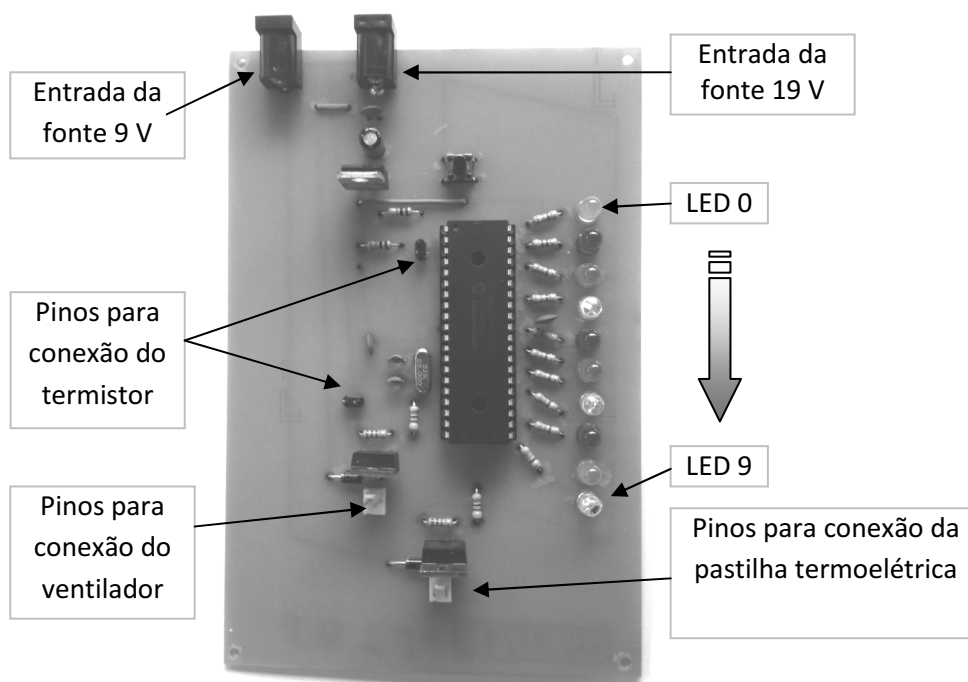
PLACA COM OS ELEMENTOS ELETRÔNICOS SOLDADOS.
